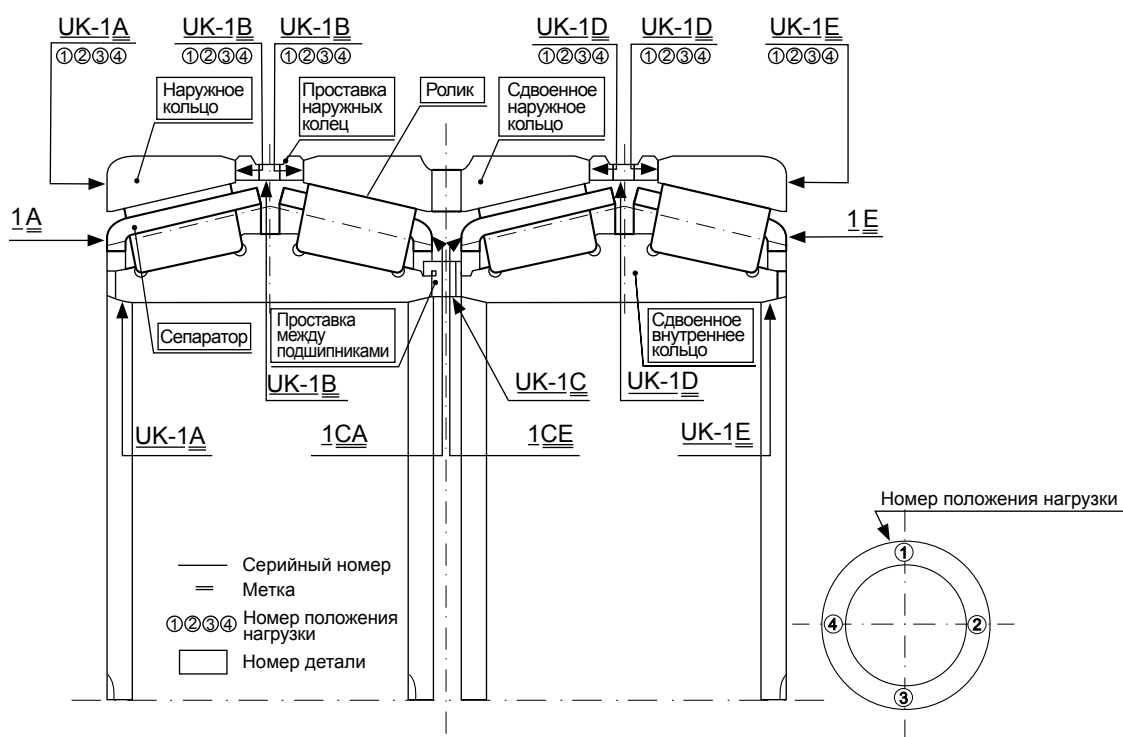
Наименование деталей и примеры маркировки (четырёхрядные конические роликоподшипники)
